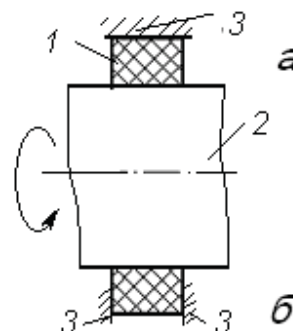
Схемы крепления упругого элемента из МР: а – по наружной поверхности; б – по боковым поверхностям; 1 – упругий пористый элемент из МР; 2 – вал; 3 – крепление
